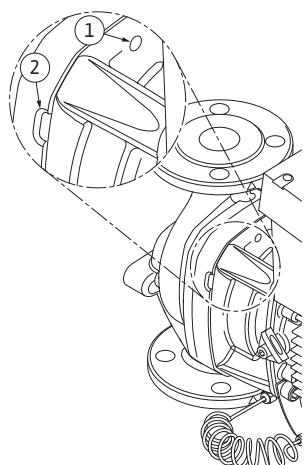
Găuri filetate și fante pentru împingerea ansamblului motor cu rotor hidraulic din carcasa pompei
